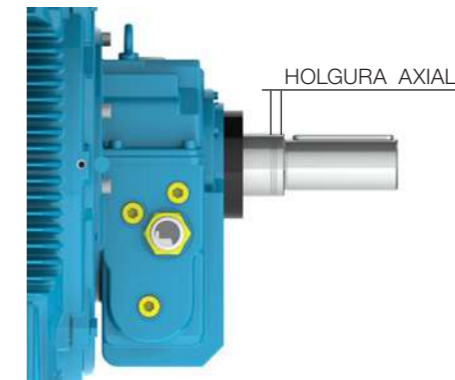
Holgura axial en motor equipado con cojinete de deslizamiento.
